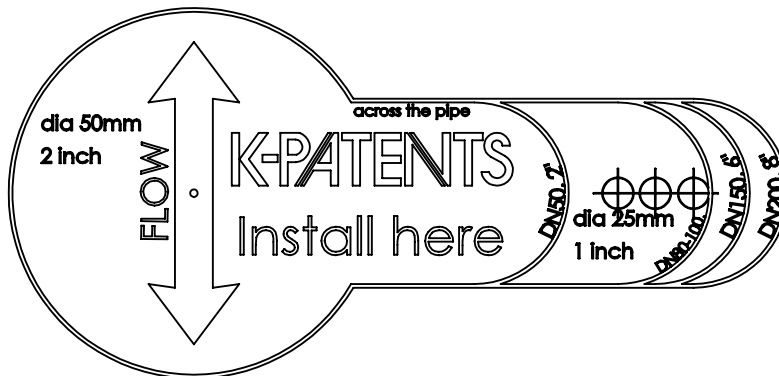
Autoadhesivo con instrucciones para instalar la válvula de aislamiento Safe-Drive™
